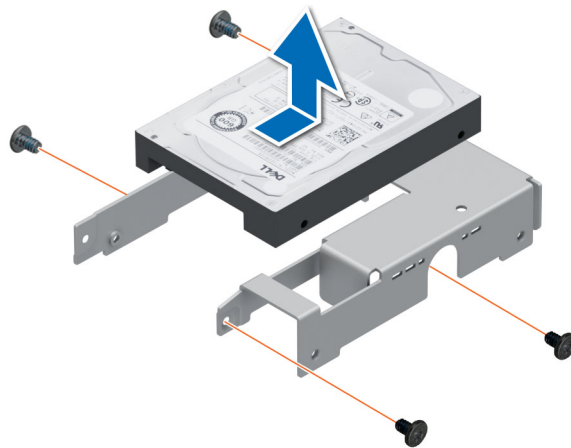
Entfernen eines 2,5-Zoll-Laufwerks aus dem 3,5-Zoll-Laufwerksadapter
